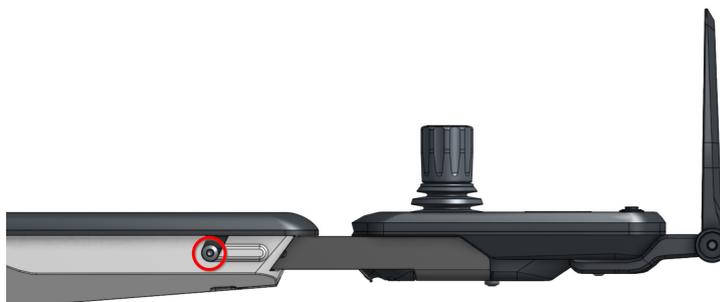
Zu lösende Schrauben, um die Position der Steuerkonsole zu verstellen (beidseitig lösen)
